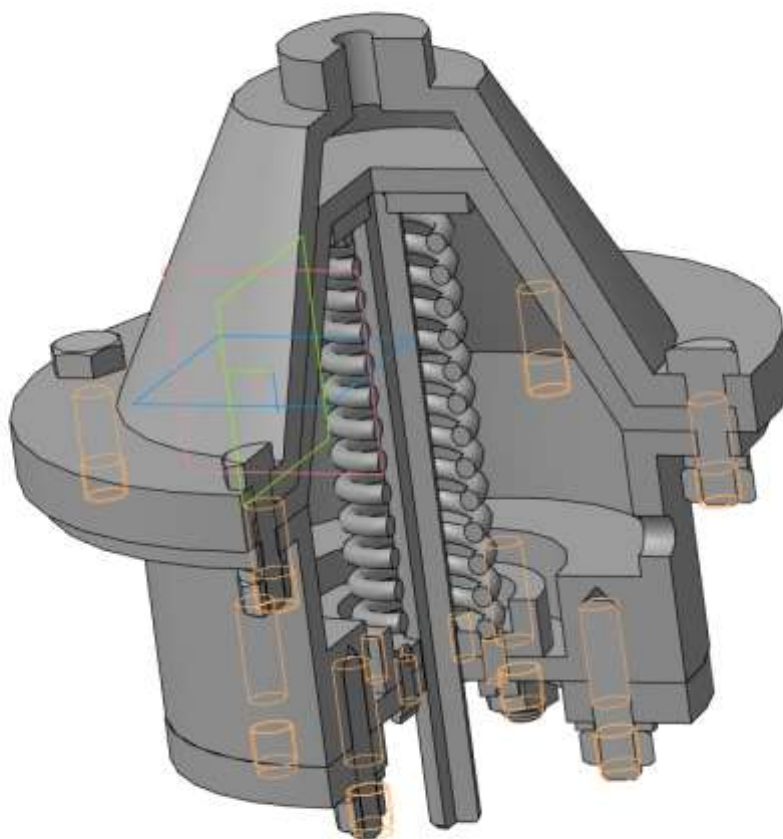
Камера Диафрагменная, 3D сборка – общий вид
